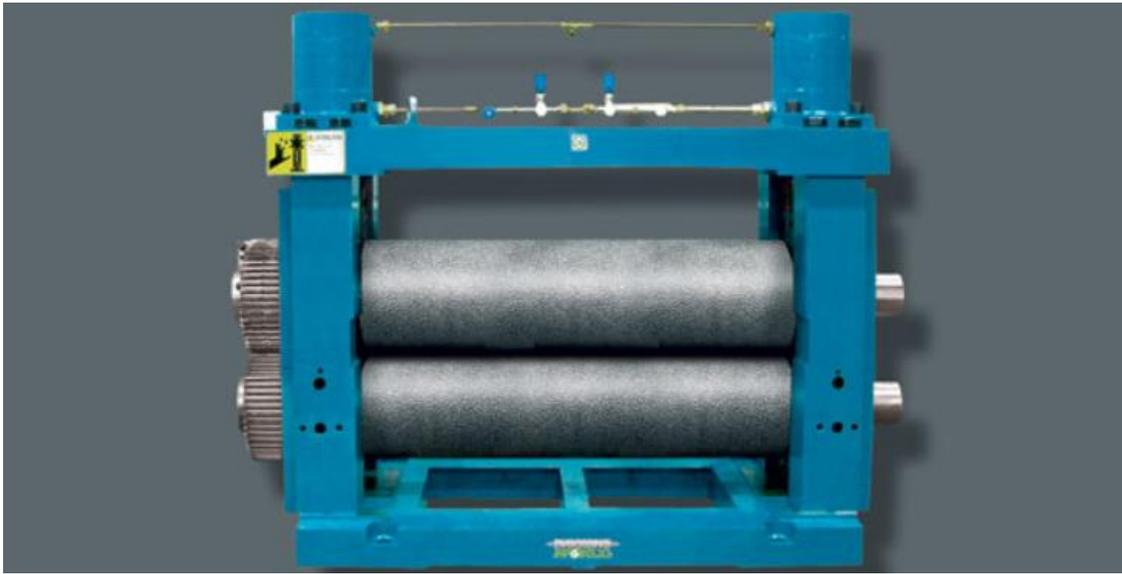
Máquina de gofrado de la empresa Embossing World [10].
